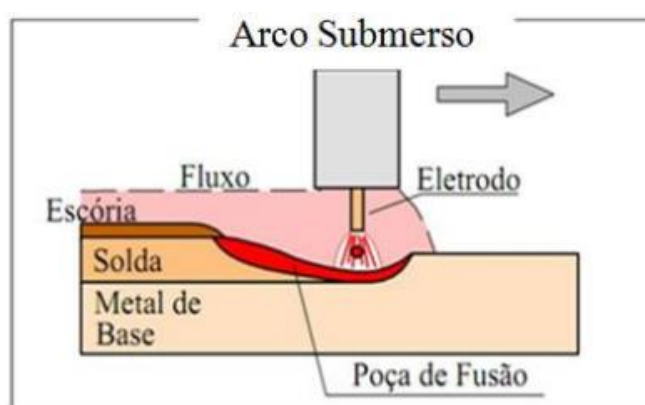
Ilustração do processo de soldadura por arco submerso [5]
